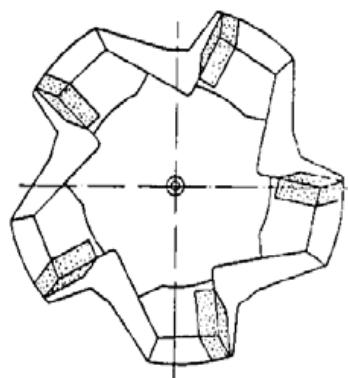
Зубці монолітної торцевої фрези з напаяними пластинами твердого сплаву
